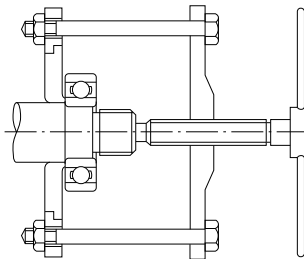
Demontage des Innenrings mit Abziehwerkzeug (1)
